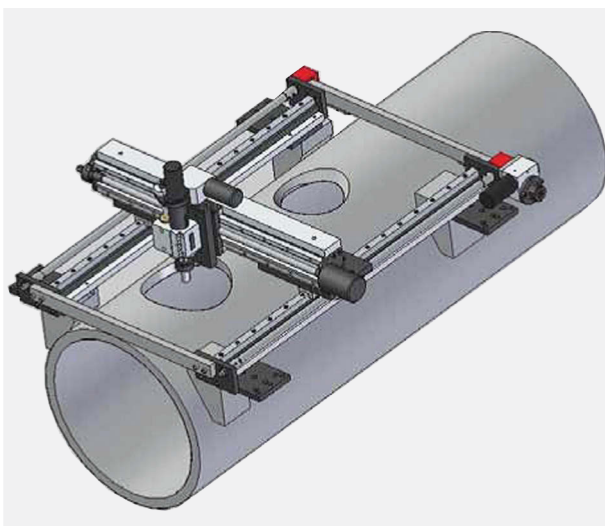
Мобильный фрезерный станок для обработки отверстий резервуаров
